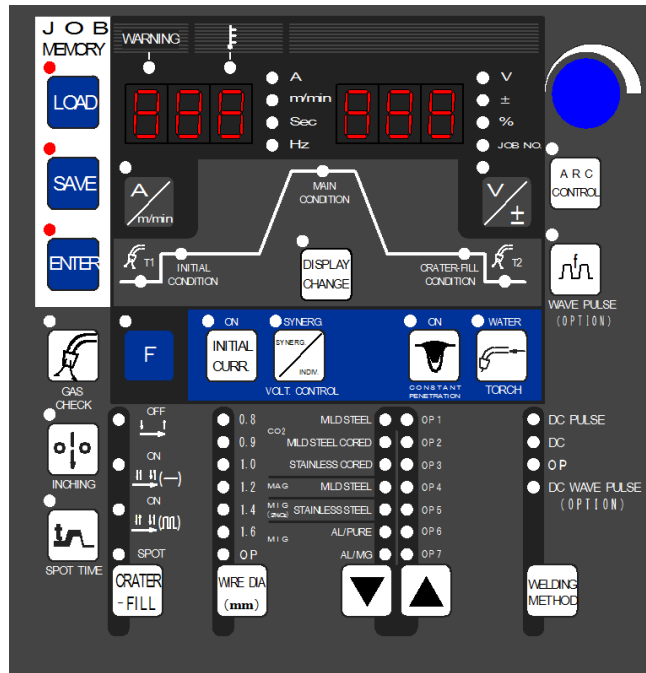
17 Robotlu Kaynak Prosesinde Çalışan Kaynak Makinaları
